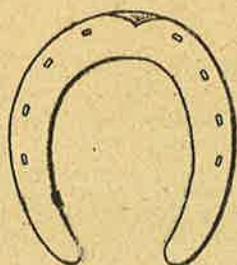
Ferradura francesa, posterior esquerda, face superior com pinção no bordo externo
